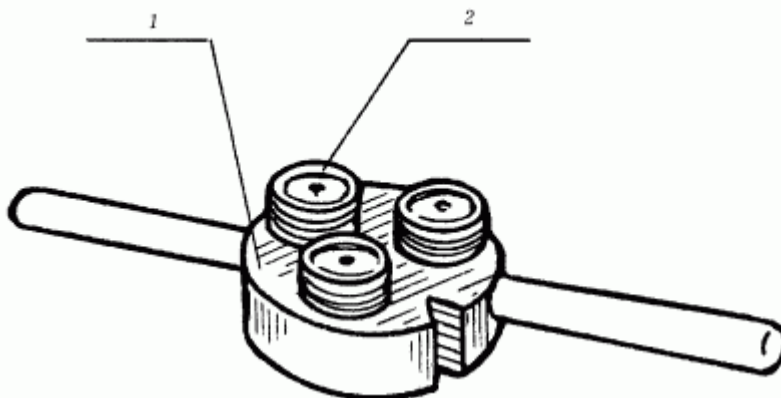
Резьбонакатная плашка: 1 – корпус; 2 – накатные ролики с резьбой
